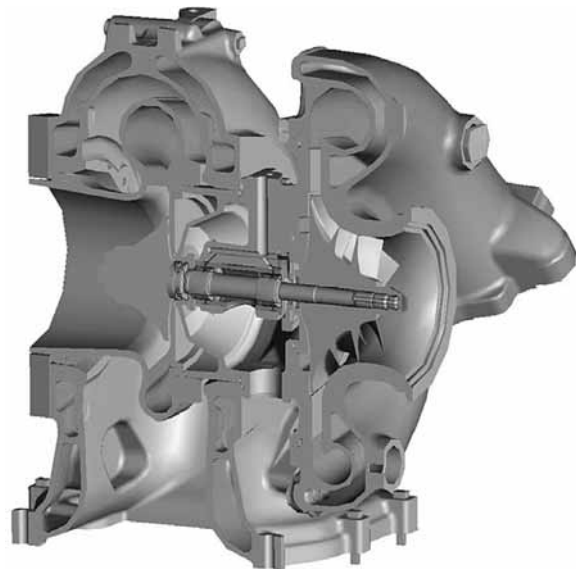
Турбокомпрессор типа ZR фирмы MTU с охлаждаемыми корпусами
